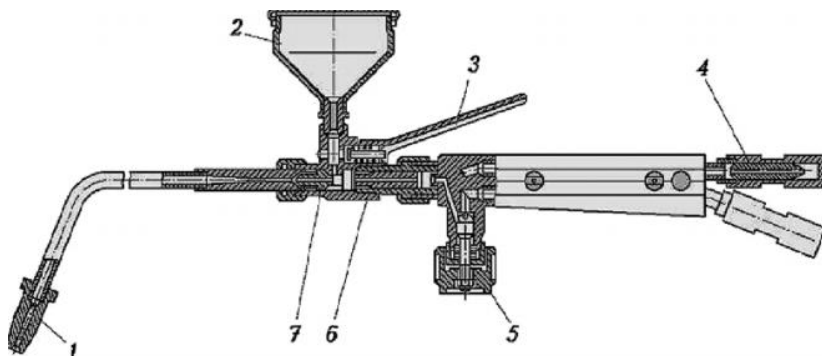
Устройство горелки марки ГН-2 для газопорошковой наплавки:
